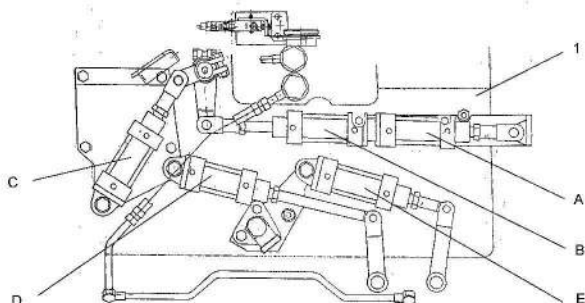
Пневматическое управление коробкой передач: 1 – коробка передач; А, В – пневмоцилиндры привода режимной муфты прямого хода; С – пневмоцилиндр включения заднего хода; D – пневмоцилиндр режимной муфты раздаточного вала; Е – пневмоцилиндр включения заднего моста.
